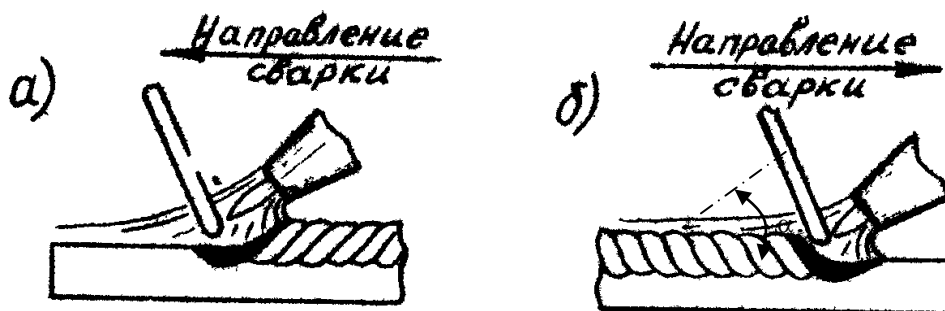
Схемы левой (а) и правой (б) способов газовой сварки
